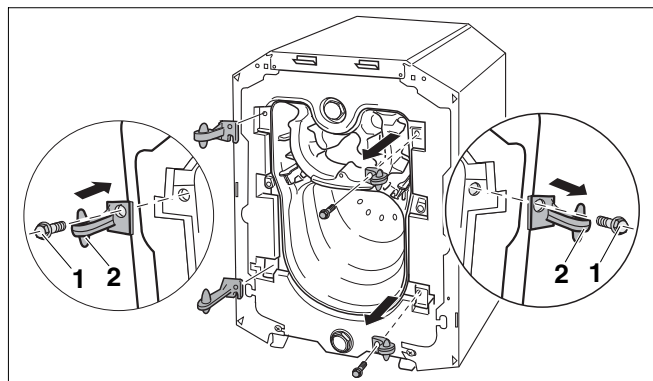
Cambiar la posición de la puerta del quemador (lado del cuerpo de la caldera)
